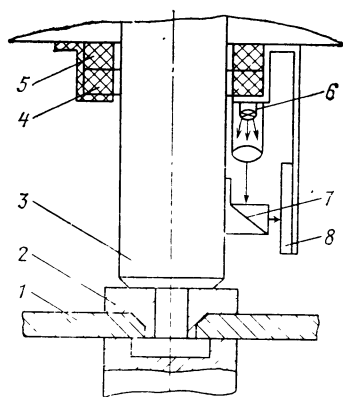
Схема оптического устройства контроля режима сварки
